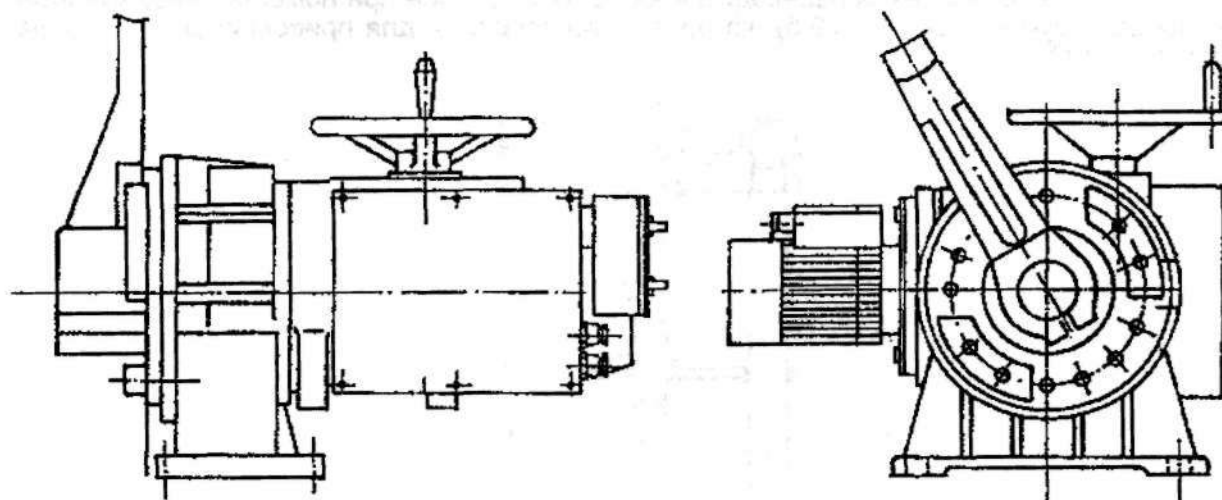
Электрический рычажный привод MODACT CONTROL MPS чертеж
